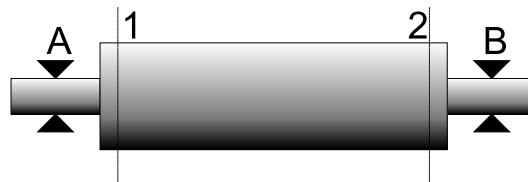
Rotor avec 2 plans de mesure et 2 plans de correction
